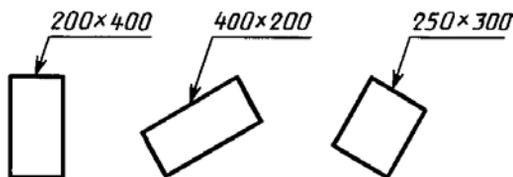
Обозначения размеров детали или отверстия прямоугольного сечения
